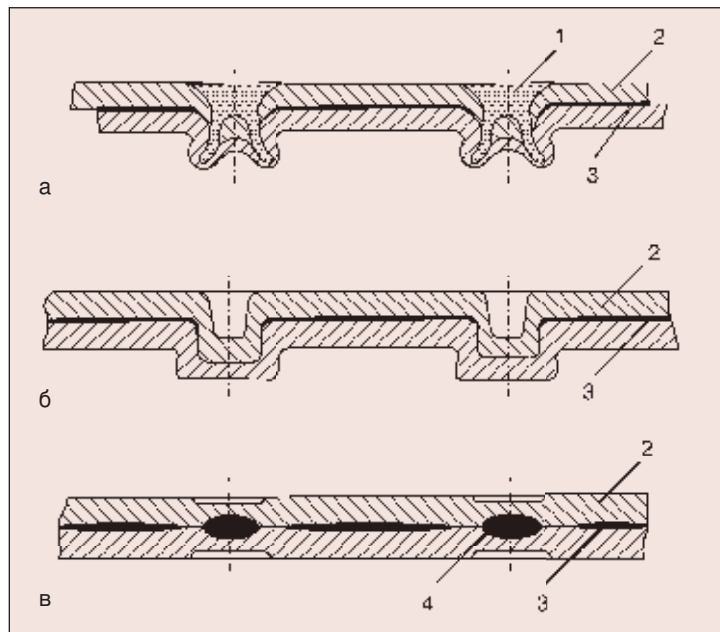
Гибридные клее-механические соединения: а — соединение полыми заклепками; б — клинч-соединение; в — точечное сварное соединение (1 — полая заклепка; 2 — соединяемые листы; 3 — прослойка клея; 4 — сварная точка)
